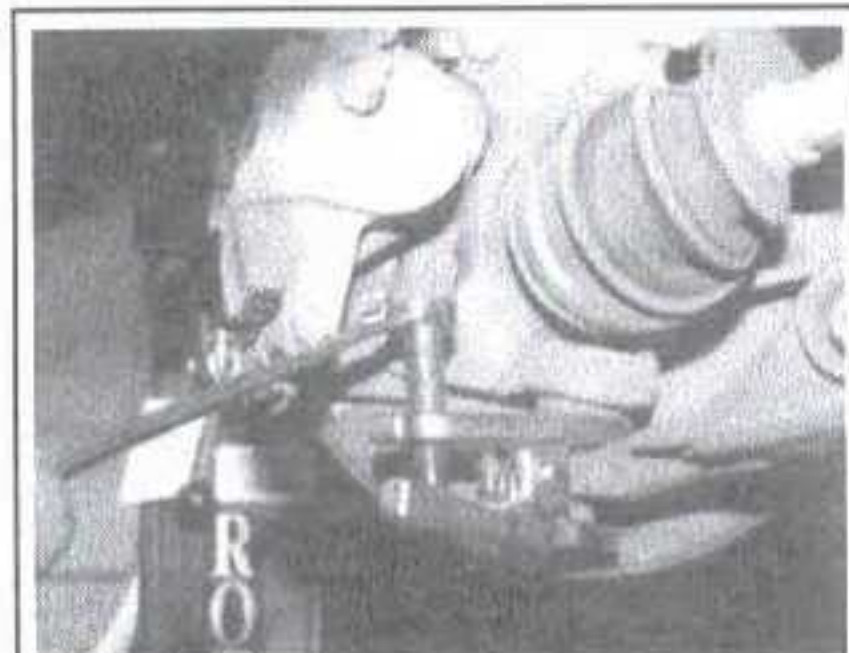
Снимите нижний шаровой шарнир в сборе при помощи съемника шаровых шарниров/поперечных рулевых тяг — показана модель CR-V
